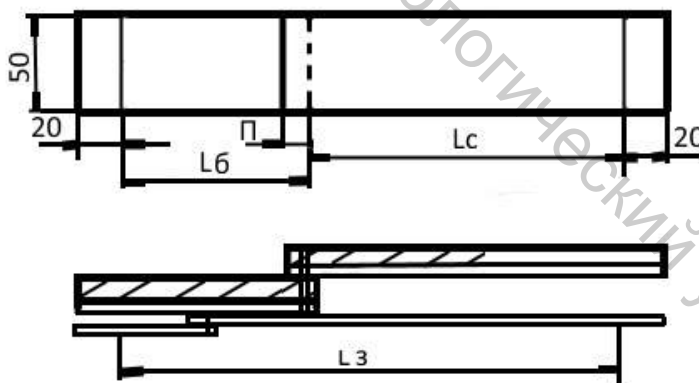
Схема определения длины образцов для расчета деформации заготовки и способа их соединения
